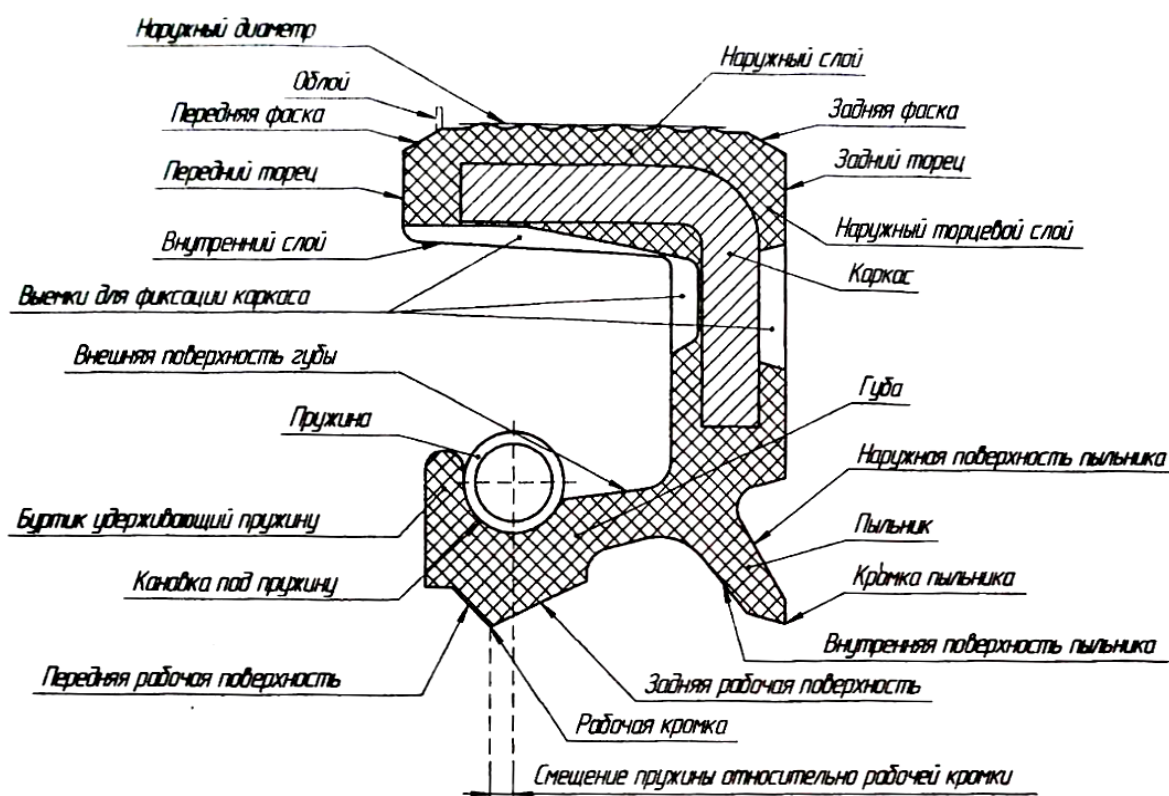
Конструкция сальника первичного вала коробки передач
